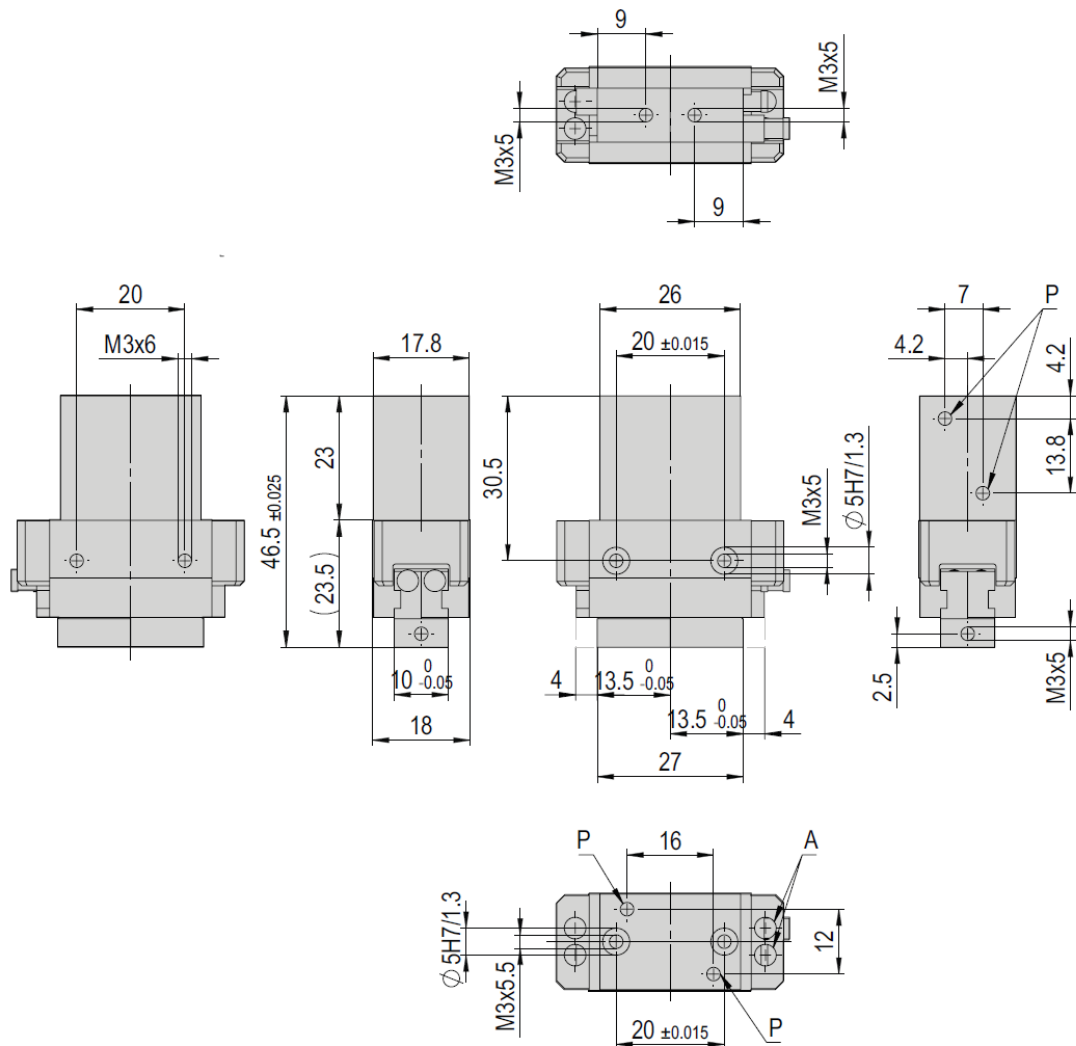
Masszeichnung Präzisionsgreifer PG 16 NC & PG 16 NO
